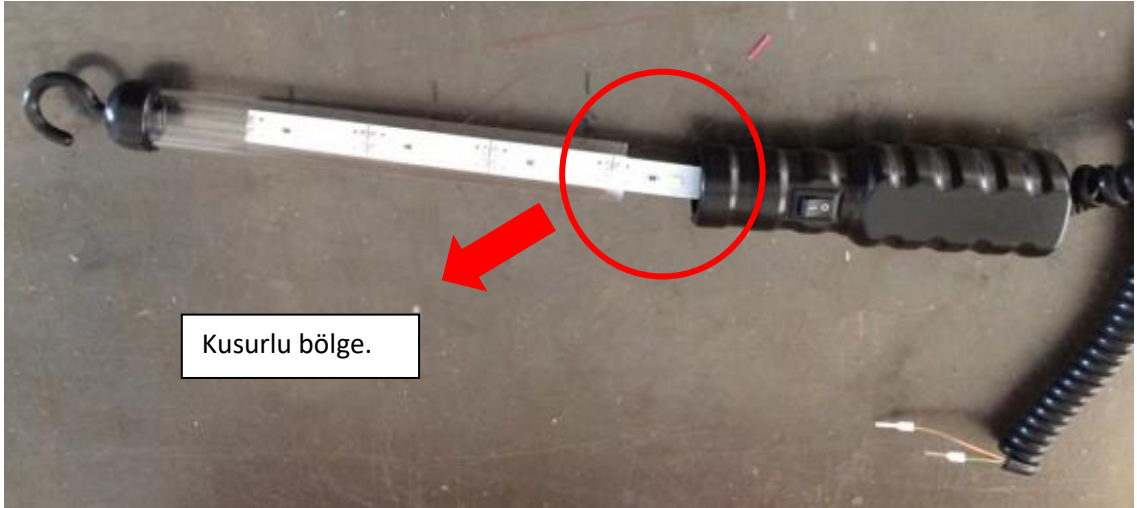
48V DC Acil Aydınlatma İç Montajı Montajı
